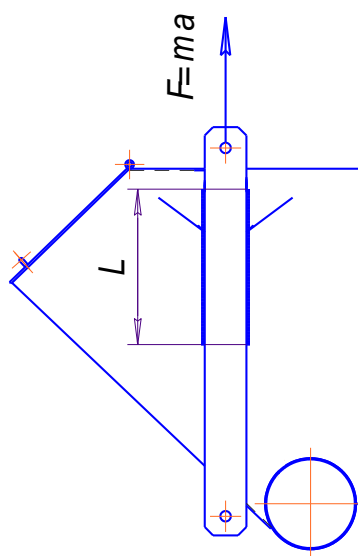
Схема сварного соединения пластины и бункера
